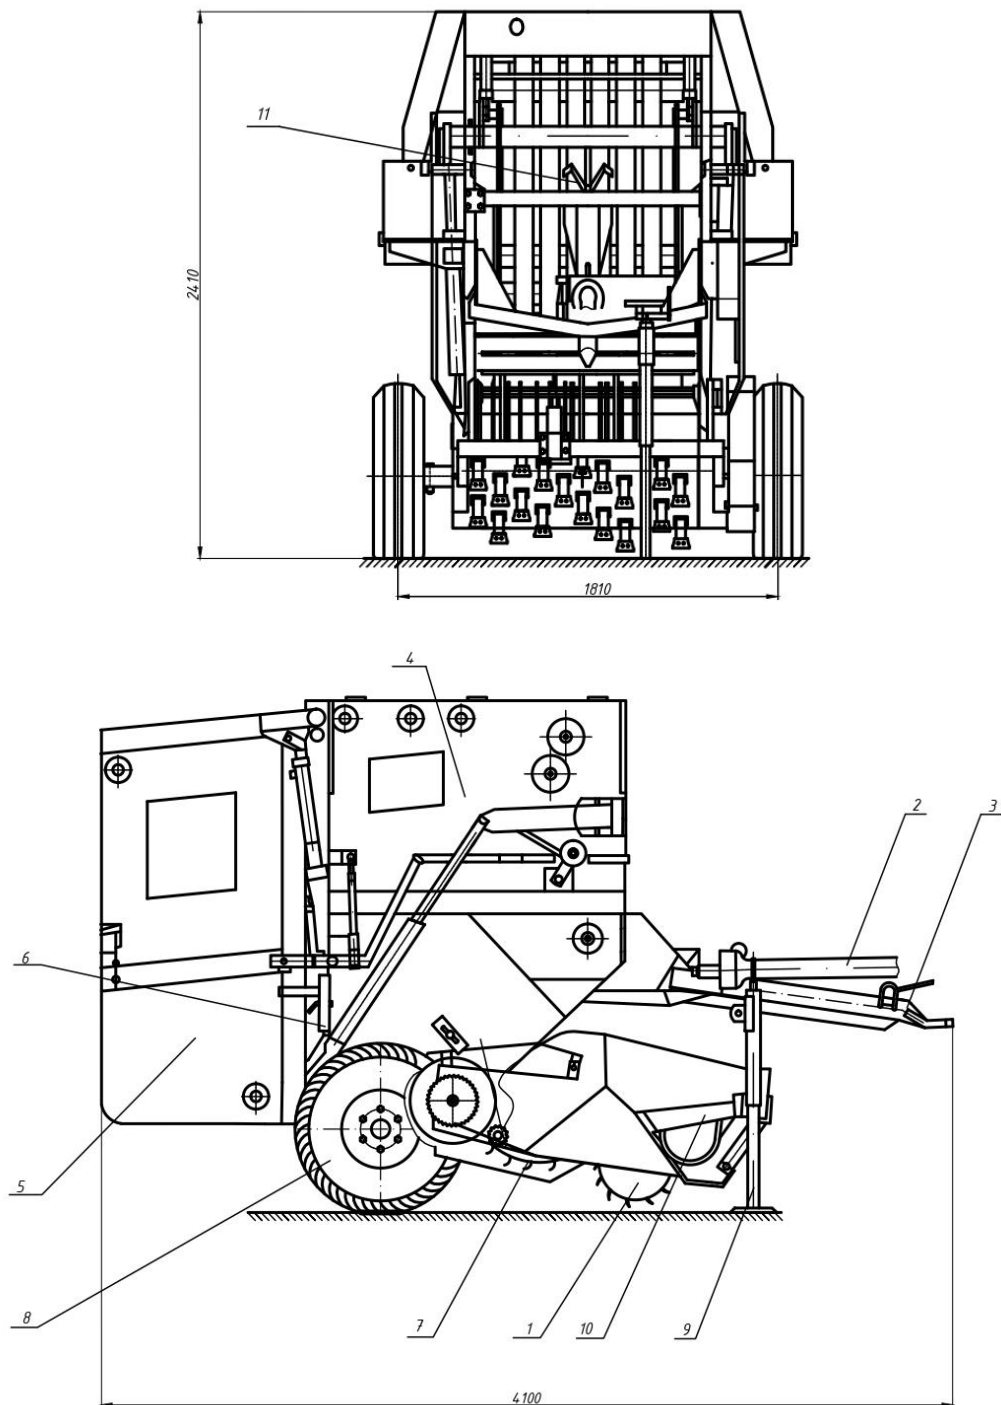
Принципова схема модернізованої причіпної машини для формування тюків деревини: 1 – ротор з ножами; 2 – привод; 3 – сниця; 4 – камера пресувальна; 5 – задній клапан; 6 – замок; 7 – барабан; 8 – колесо; 9 – опора; 10 – захист; 11 – обмотувач
